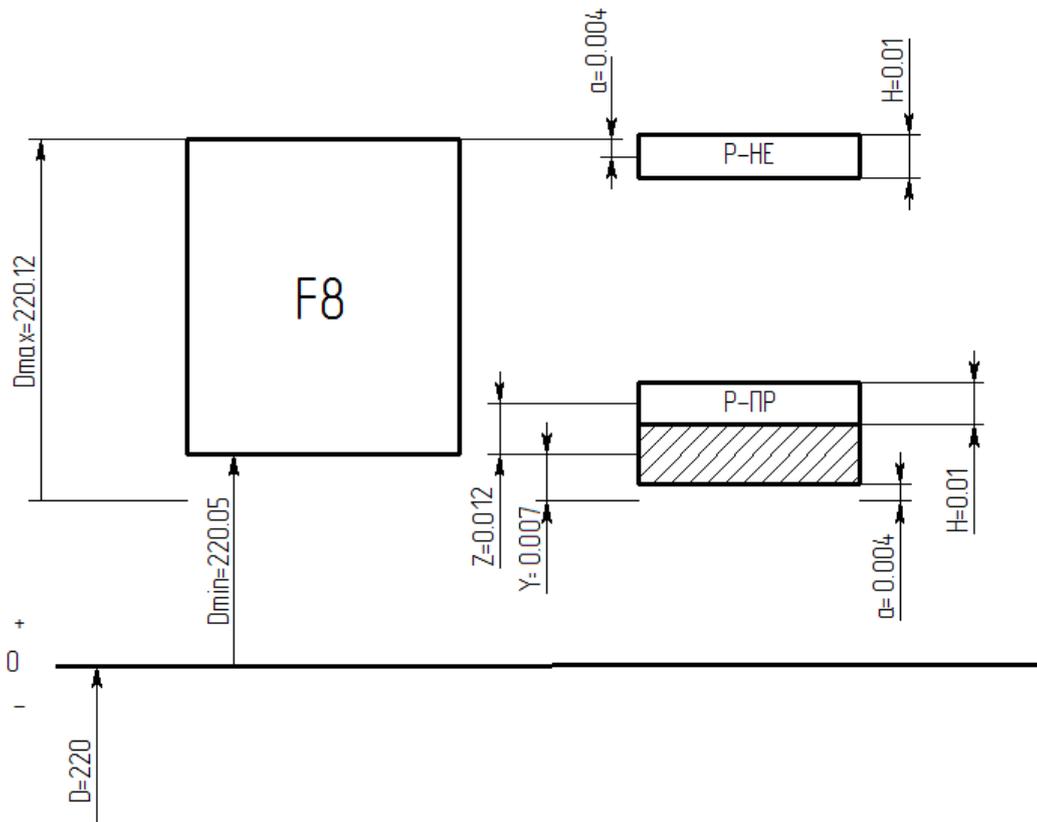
Схема расположения полей допусков калибра – пробка
